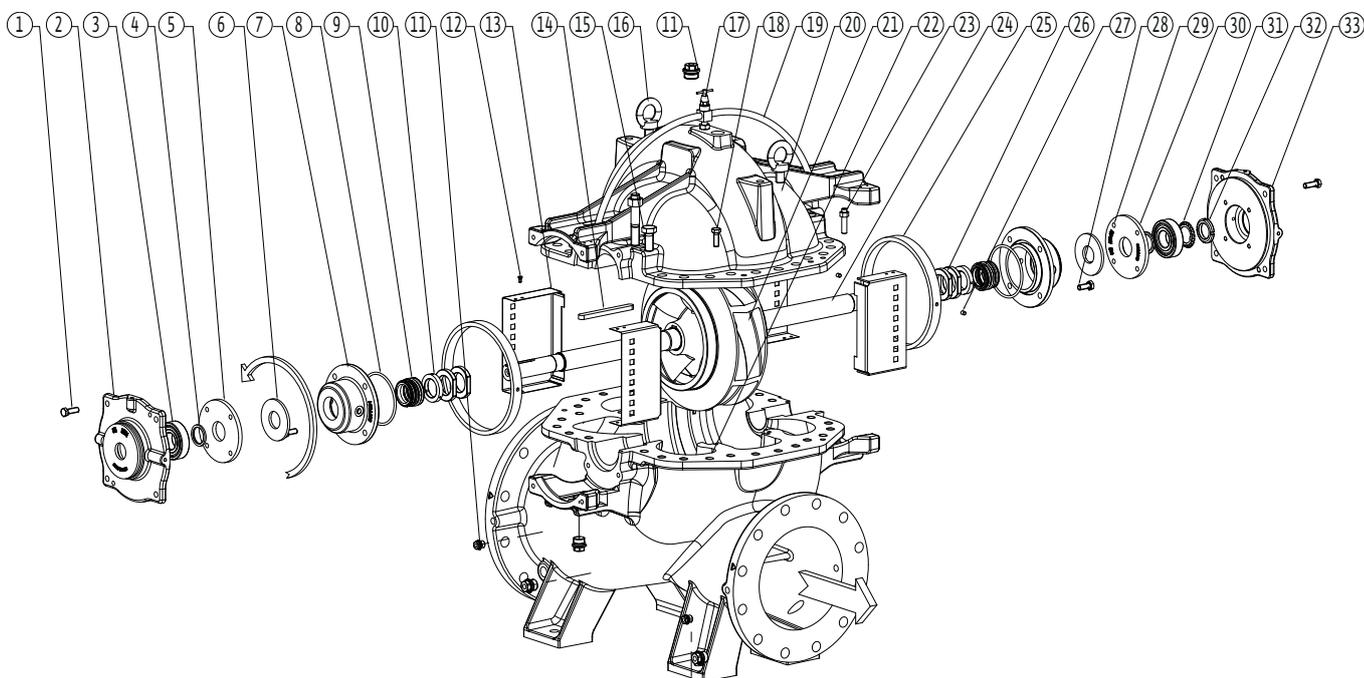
Vista despiezada del conjunto hidráulico de la Atmos TERA-SCH (ejecución del cierre mecánico sin manguitos)
